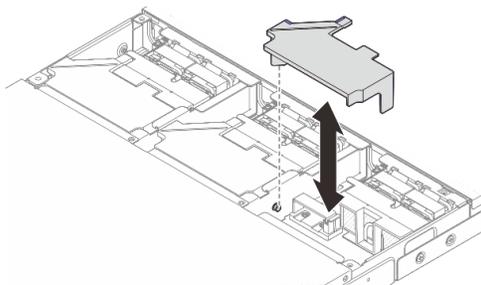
Entfernen der Luftführung für 1U3N-Gehäuse
